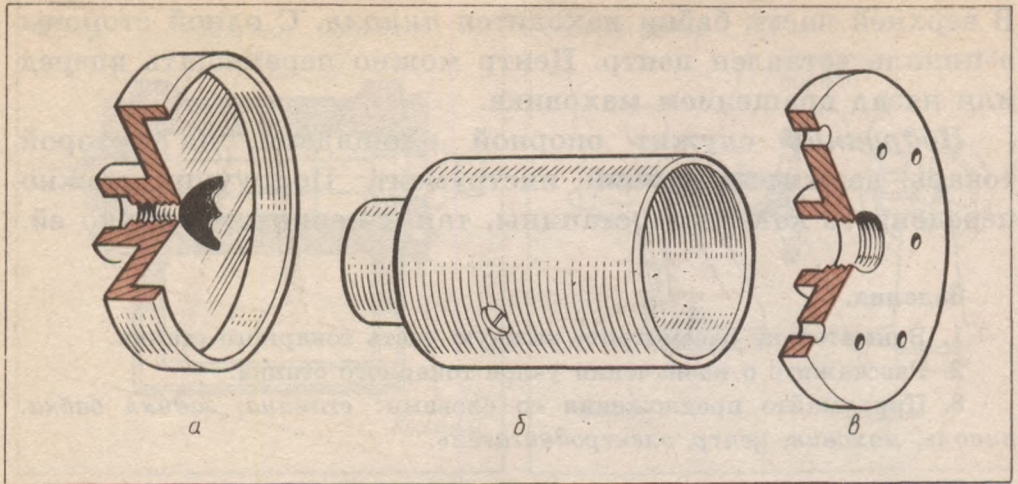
Приспособления для крепления заготовок на токарном станке: *а* — корпус с центром-вилкой; *б* — патрон; *в* — планшайба.
